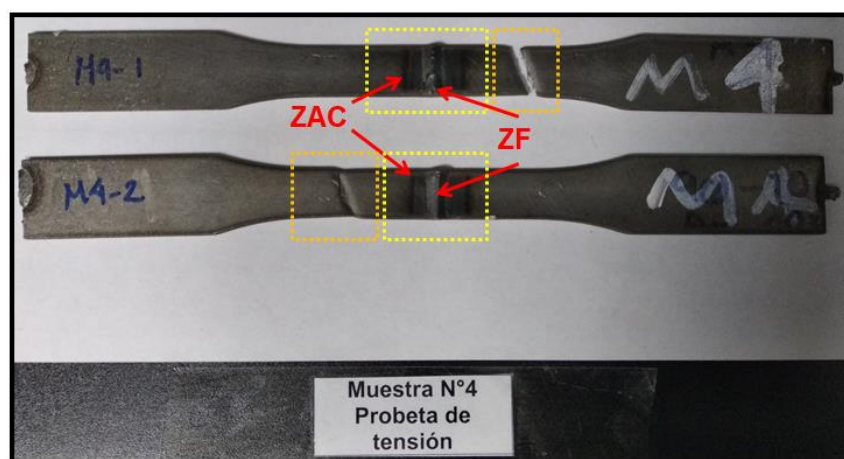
Muestra N° 4, fractura en metal base similar a metal base sin soldar.
